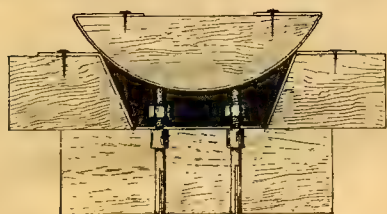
Изготовление держателя (форма и самый держатель — в разрезе).
